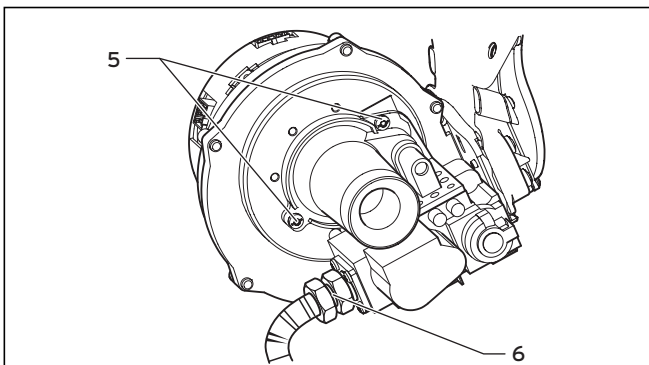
Резьбовое соединение газовой арматуры/вентилятора
